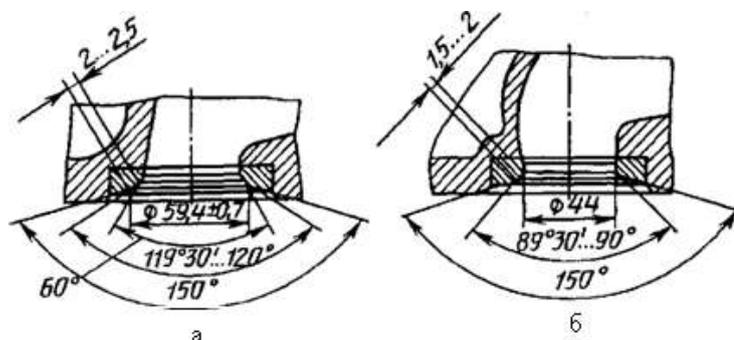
Схемы обработки седел клапанов двигателя типа ЯМЗ:
